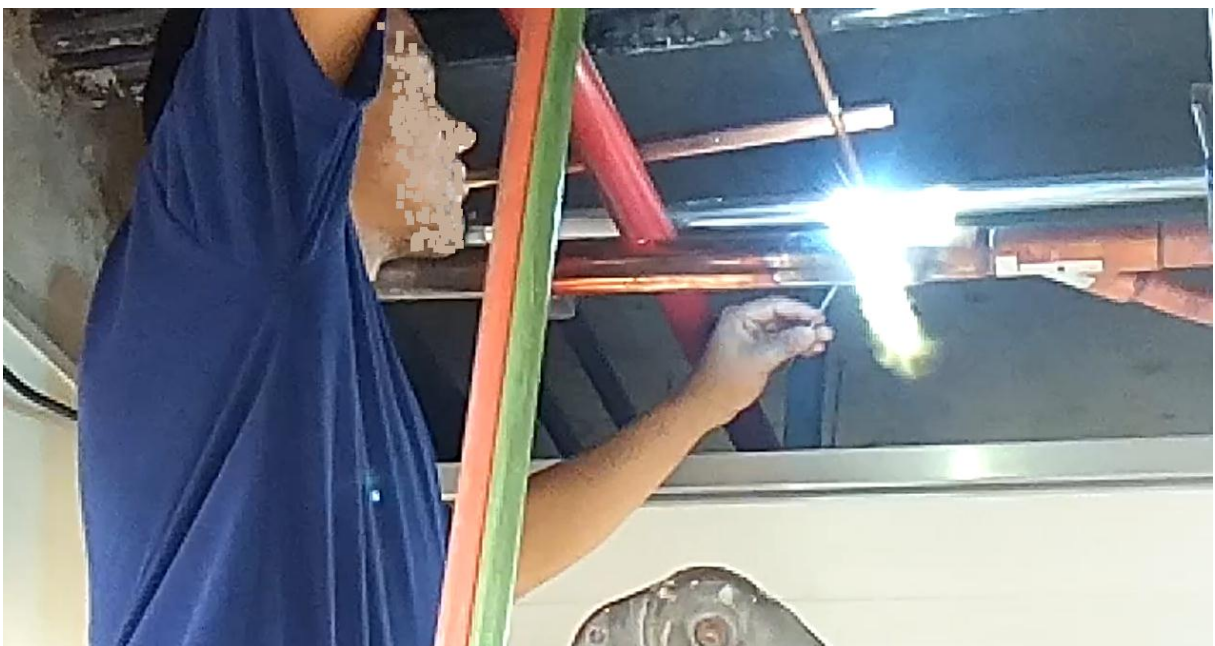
Soldador "A" realizando a solda sobre a cabeça
